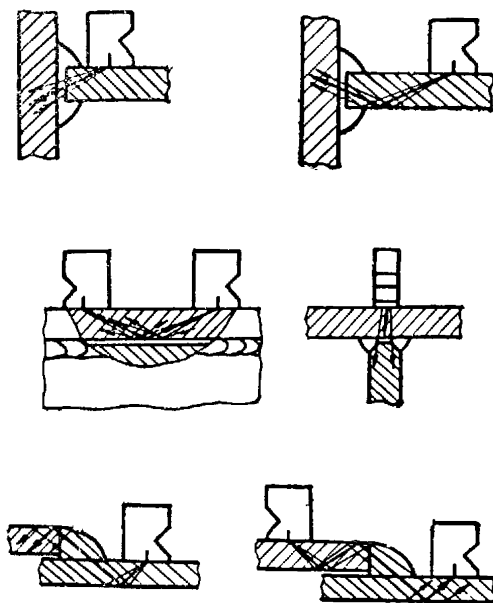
Схемы контроля тавровых и нахлесточных сварных соединений
